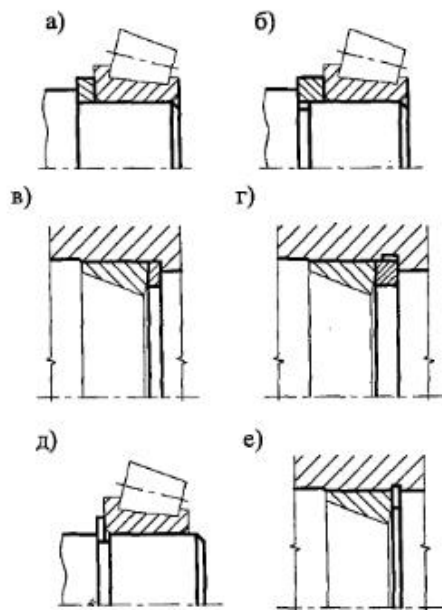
Конструктивные решения по уменьшению высоты заплечников валов (корпусов) в месте установки подшипника:
